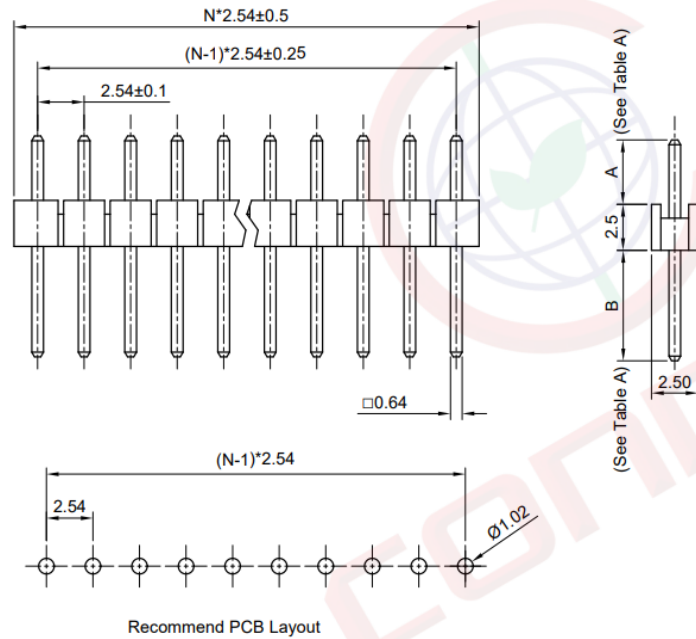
Параметры корпуса электрического соединителя PLS
